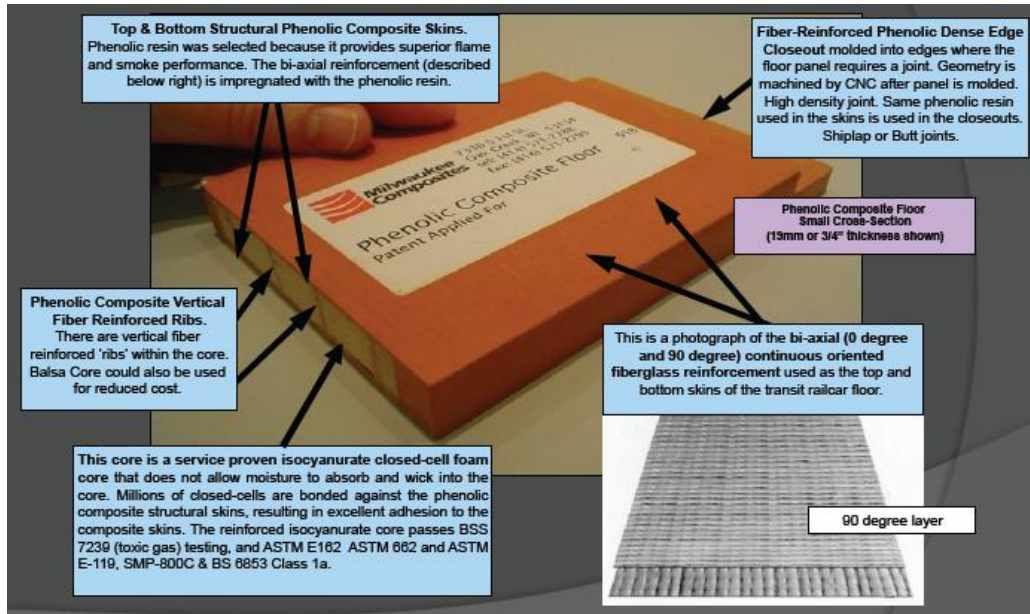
酚醛複合材地板結構(phenolic composite floor panel construction)
